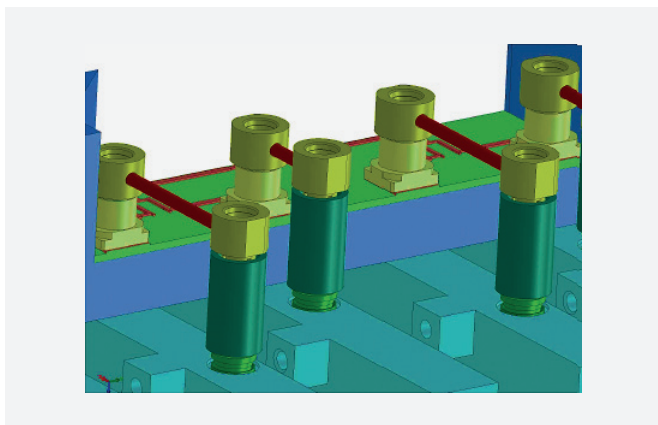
Объемный монтаж СВЧ-устройства с применением вилок для установки на печатную плату, bullet и кабельных сборок
